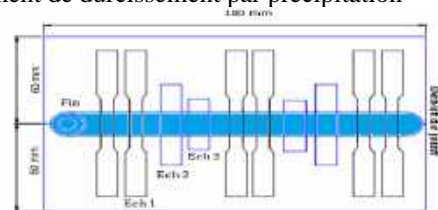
Découpe des échantillons sur les plaques soudées.
